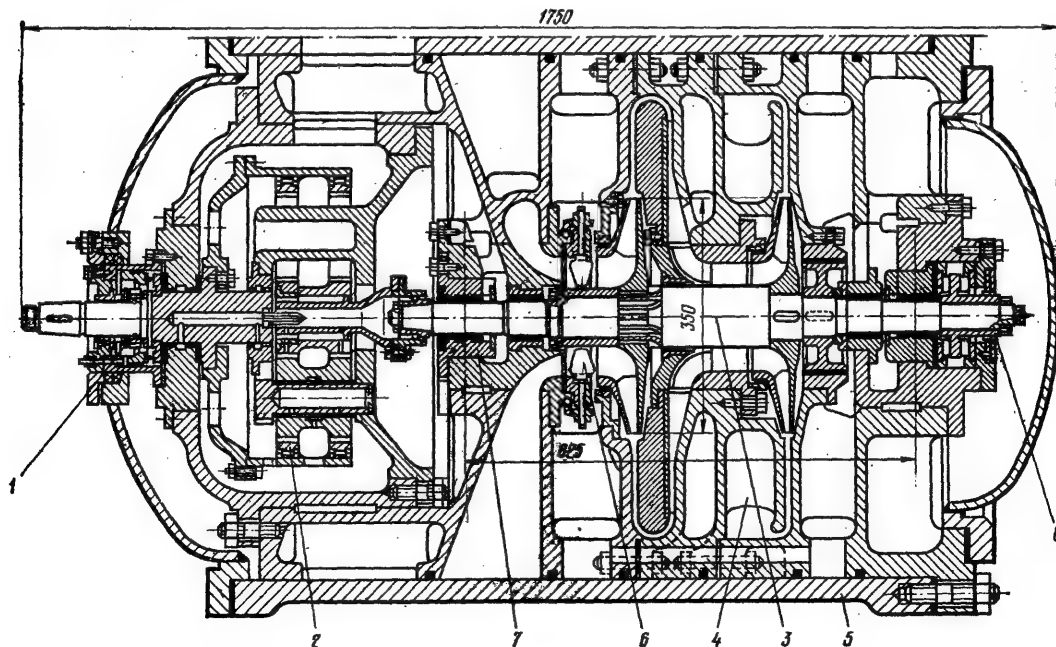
Двухступенчатый фреоновый центробежный компрессор с мультипликатором:
